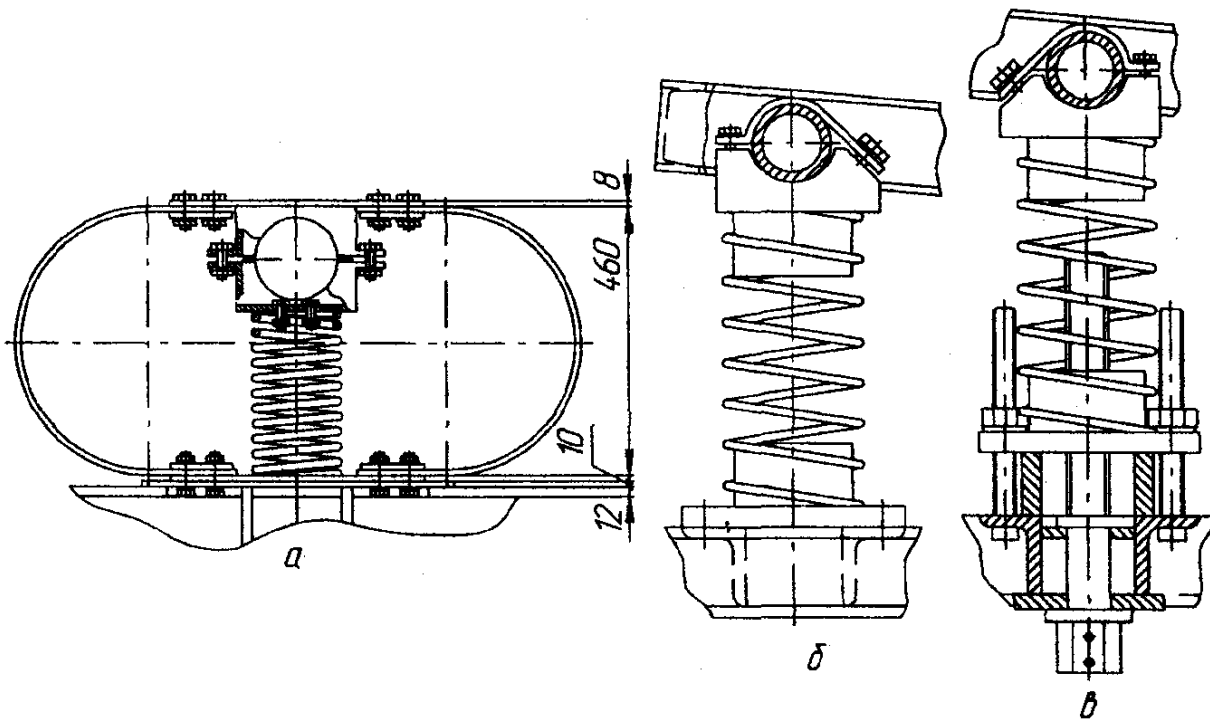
Овальные рессоры и винтовые цилиндрические пружины:
